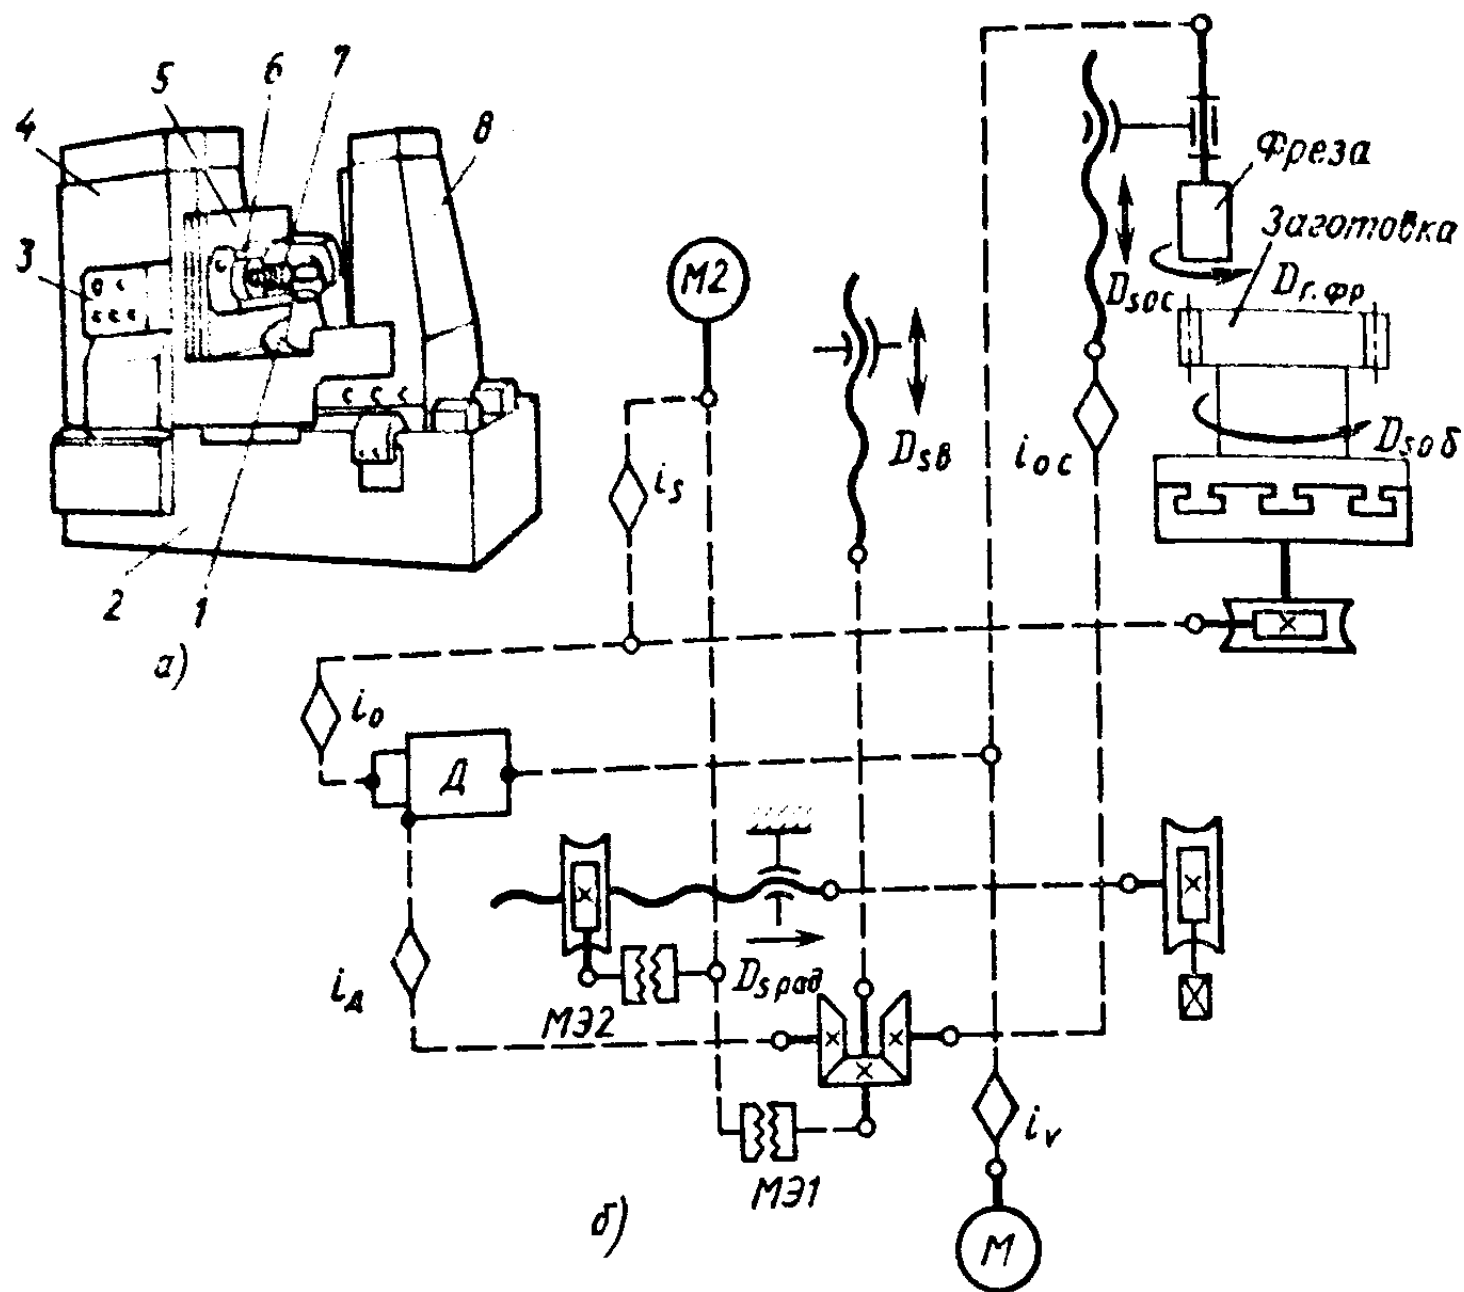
Зубофрезерный полуавтомат 53А50:
